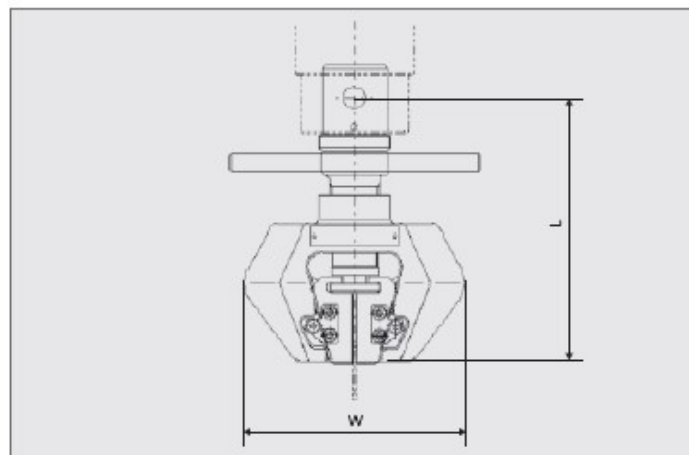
Vista Perfil Amarra Shimadzu MWG-100kNA [16]
